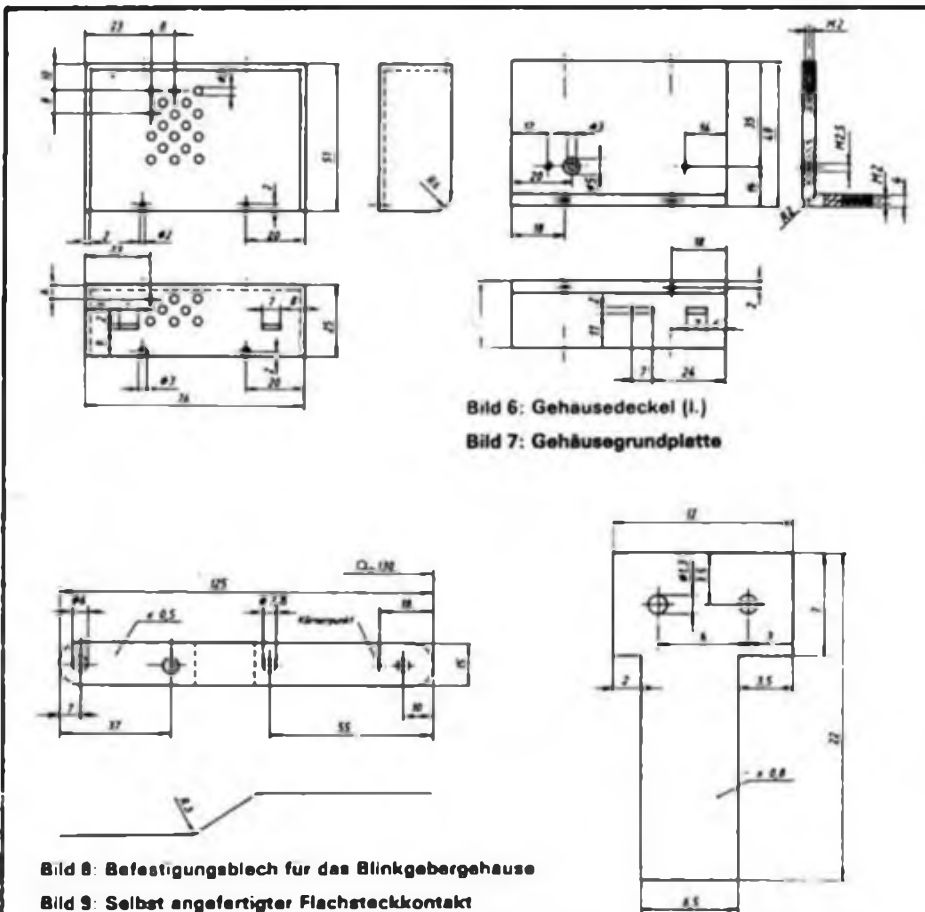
Befestigungsblech für das Blinkgebergehäuse
